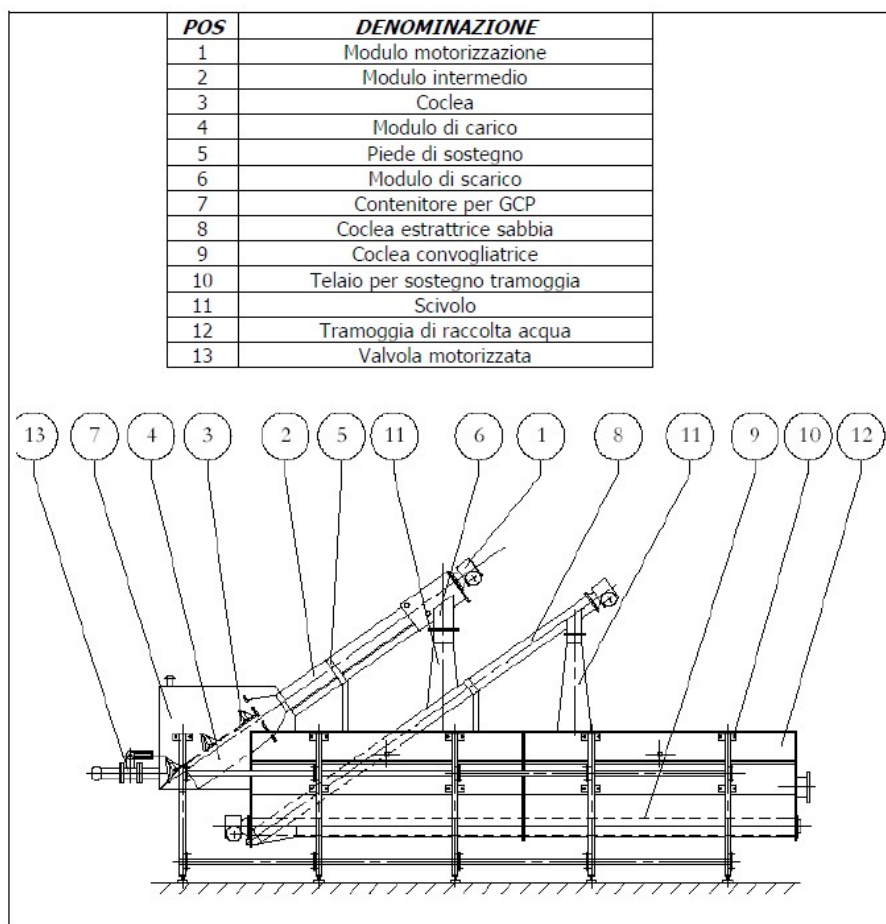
Macchina per la grigliatura, dissabbiatura e disoleatura
